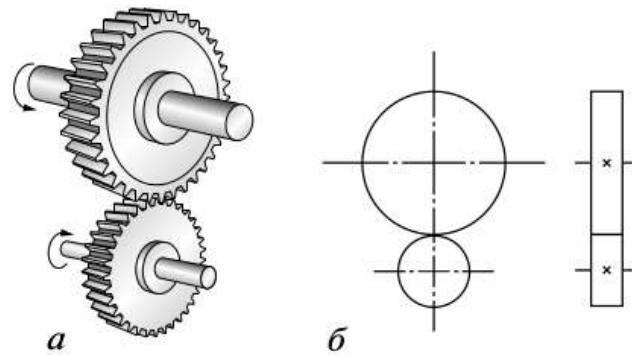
Цилиндрическая зубчатая передача: а — наглядное изображение;
